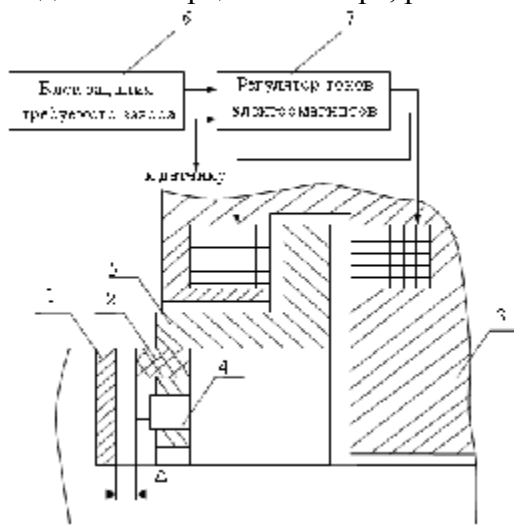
Схема управляемого электромагнитного торцевого уплотнения: 1- вращающееся кольцо уплотнения на роторе; 2 - невращающееся кольцо, установленное на корпусе - 3; 4- датчик для контроля величины зазора; 5- якорь электромагнитной системы; 6 и 7 система автоматического поддержания установленного зазора
